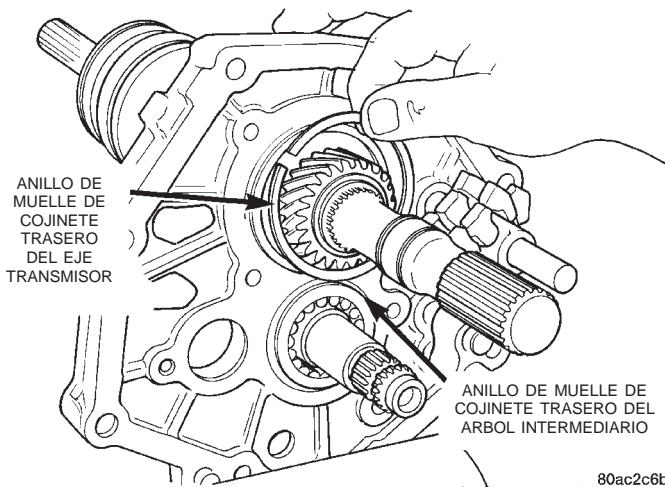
Desmontaje de anillo de muelle de cojinete trasero del eje transmisor
